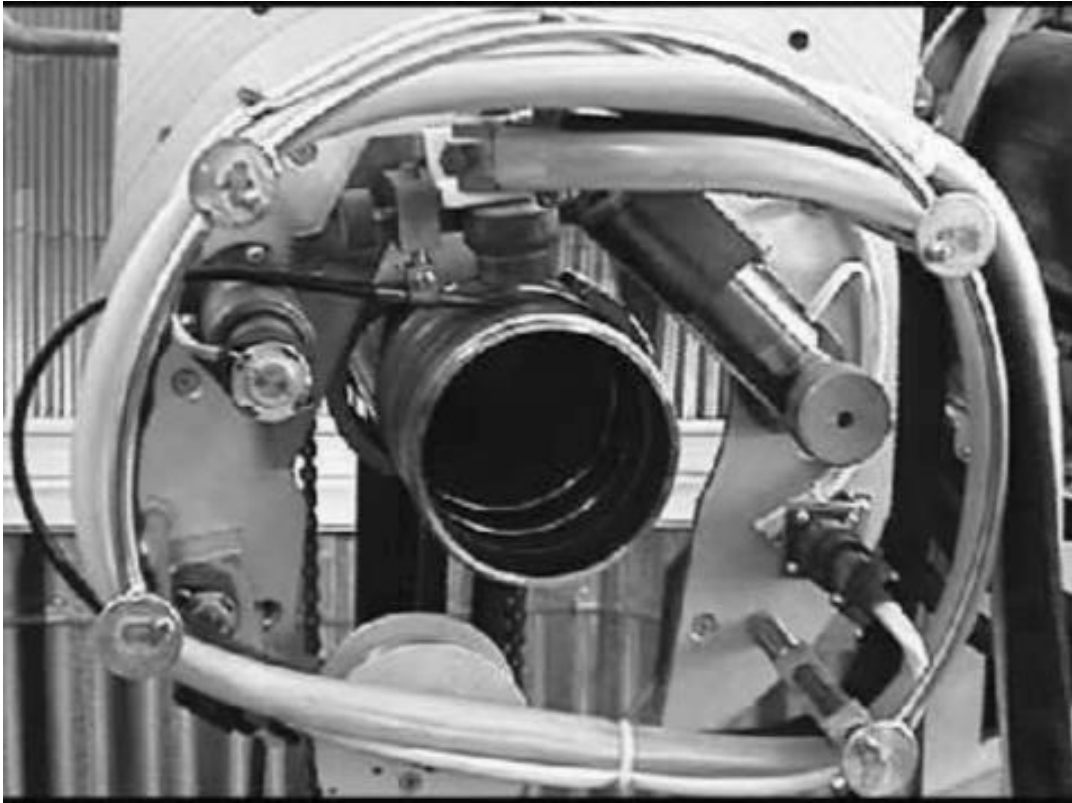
Зовнішній вигляд автоматичної головки для аргоннодугового зварювання неповоротних стиків труб
